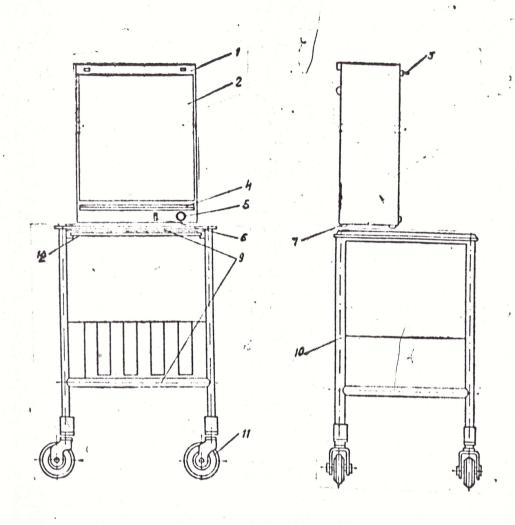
Петатоской общего назначения передвижной ПТ-48. Общий вид 1— корвус; 2— экран; 3— кронштейн; 4— лоток; 5— ручка регулировки пркости; 6— выключатель; 7— ножка; 9— полка; 10— каркас; 11— колесо; 12— полка бызбымия
